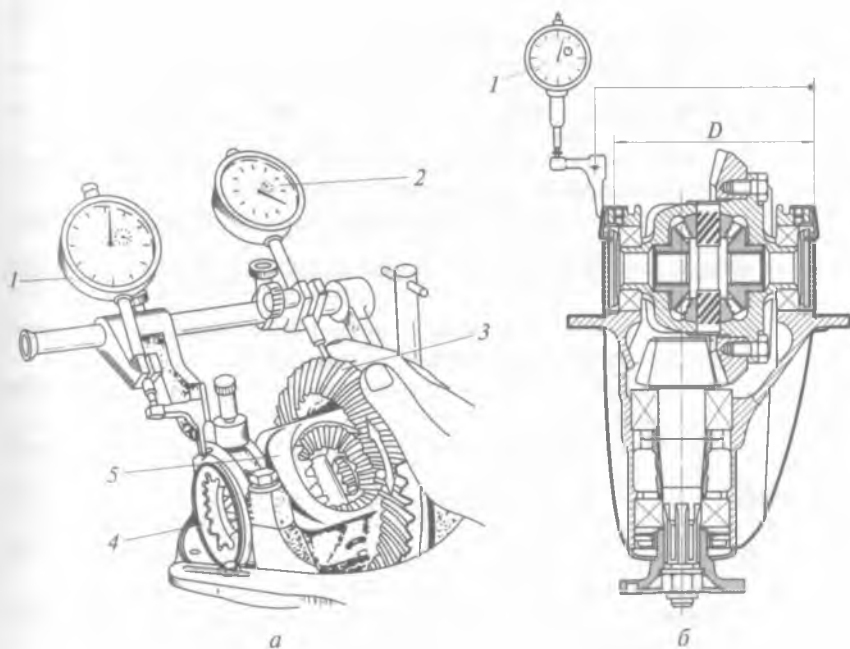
Схема регулирования зацепления зубьев колес главной передачи с помощью специального контрольного приспособления:
